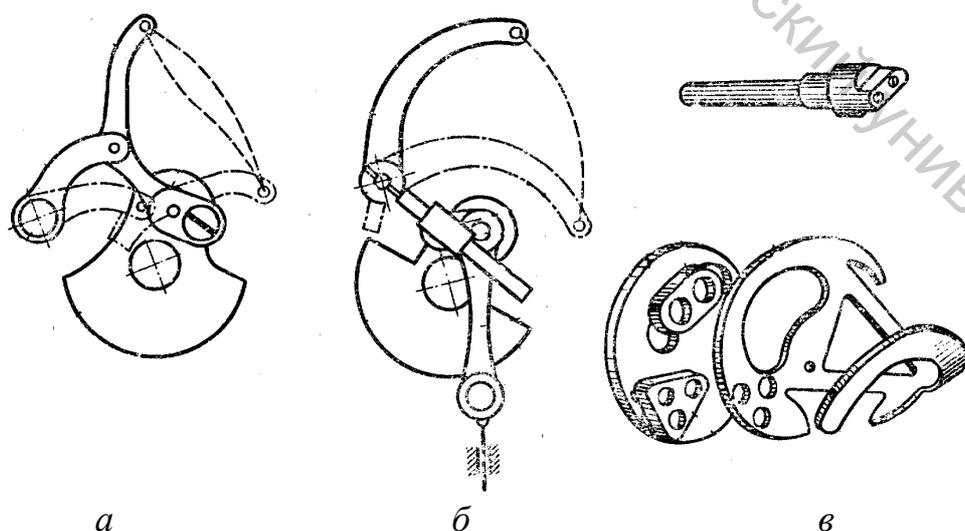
Нитепритягиватели машин челночного стежка: а – шарнирно-стержневой; б – кулисный; в - вращающийся
